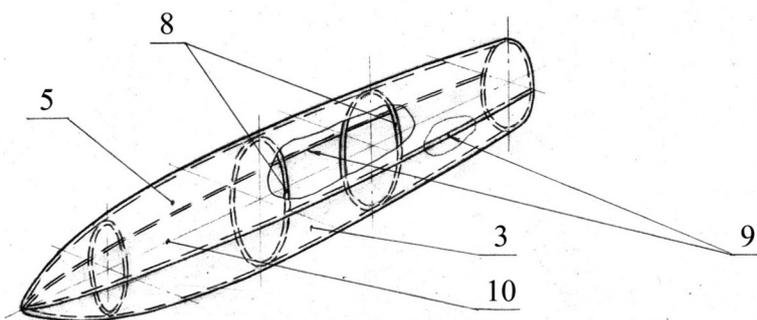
Готовый агрегат с поверхностями двойной кривизны и вклеенными элементами каркаса
